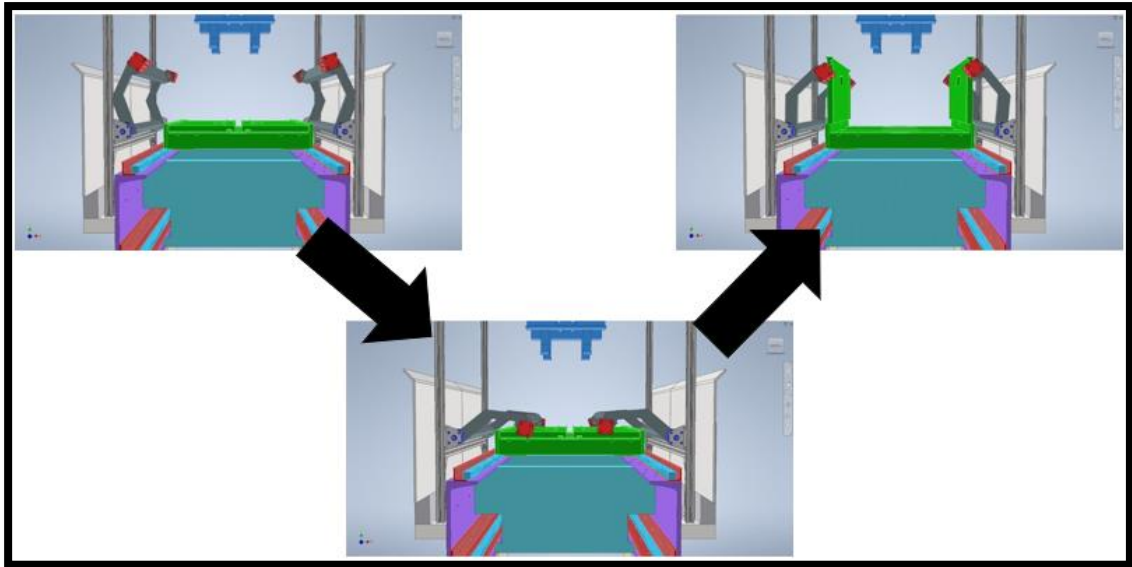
Secuencia de la primera parte del mecanismo de ensamblaje de gavetas plegables
